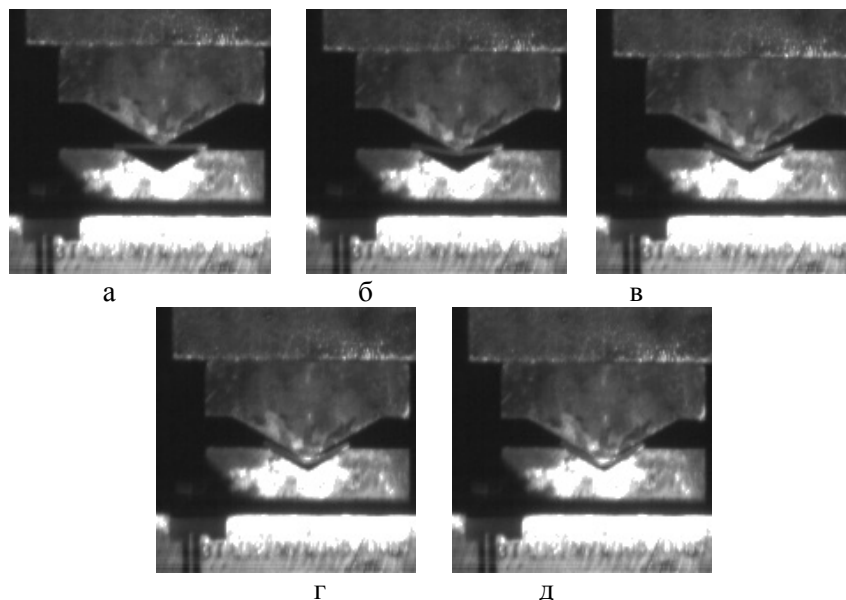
Раскадровка видеозаписи процесса гибки заготовки на молоте (копре) с углом гибки  $120^\circ$ : а – соприкосновение пуансона и заготовки, начало гибки заготовки; б – в – этапы гибки заготовки; г – окончание гибки заготовки
